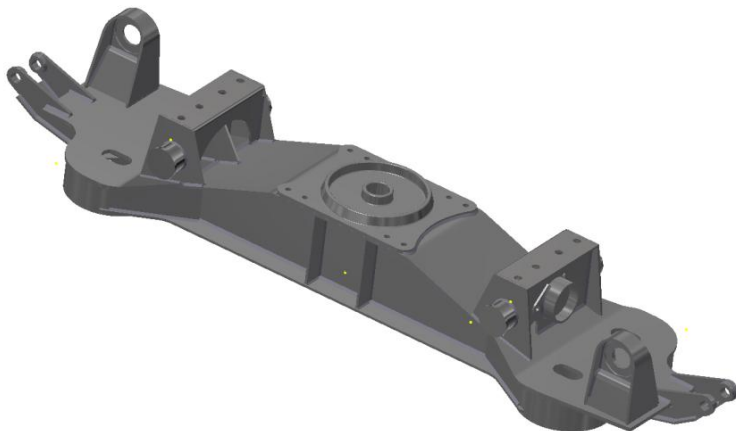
Трехмерная модель сварной конструкции наддрессорной балки тележки КВЗ-ЦНИИ
